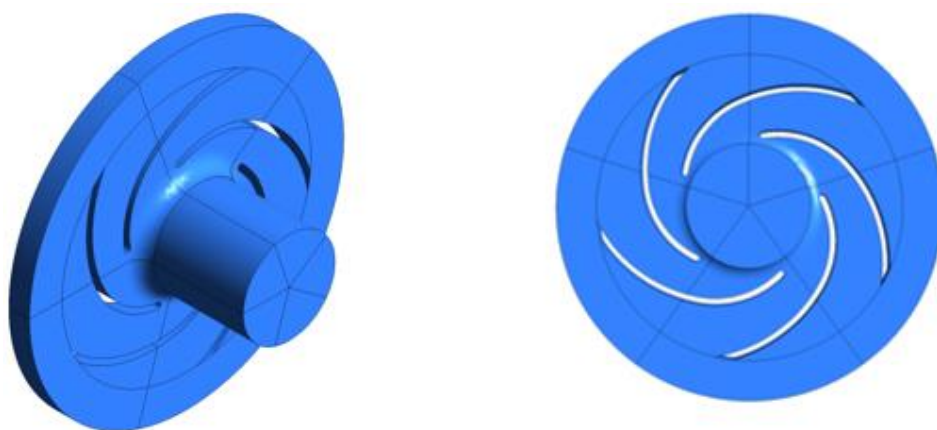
Rotor completo. À esquerda a vista isométrica. À direita a vista frontal (autor)
